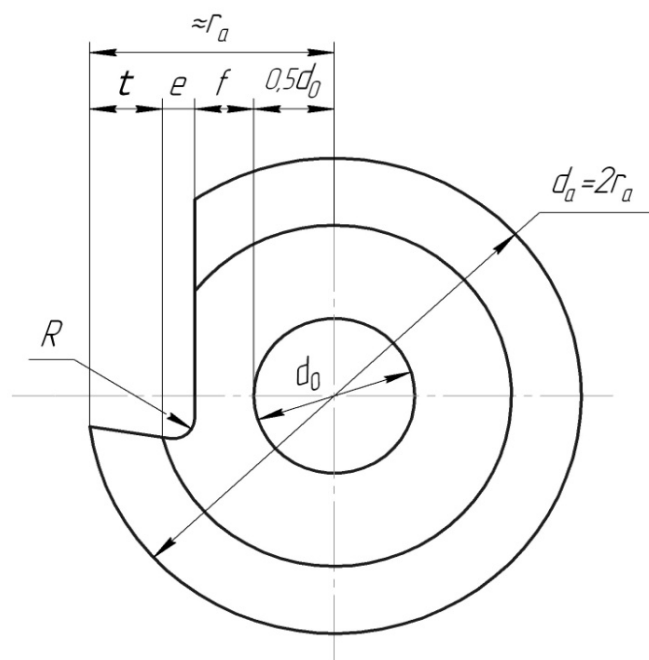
Схема к расчету наружного диаметра круглого фасонного резца
